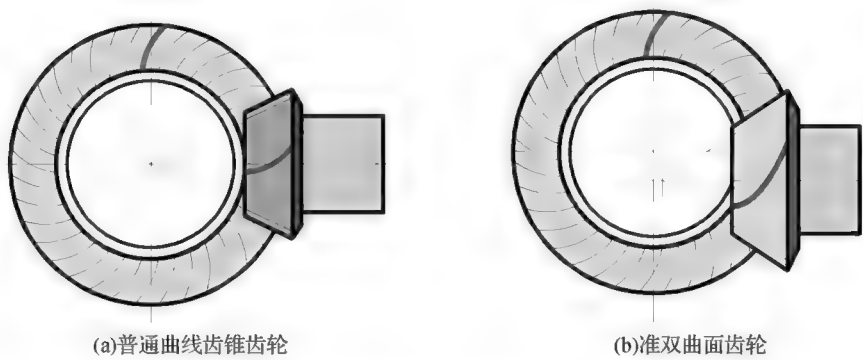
普通曲线齿锥齿轮和准双曲面齿轮
